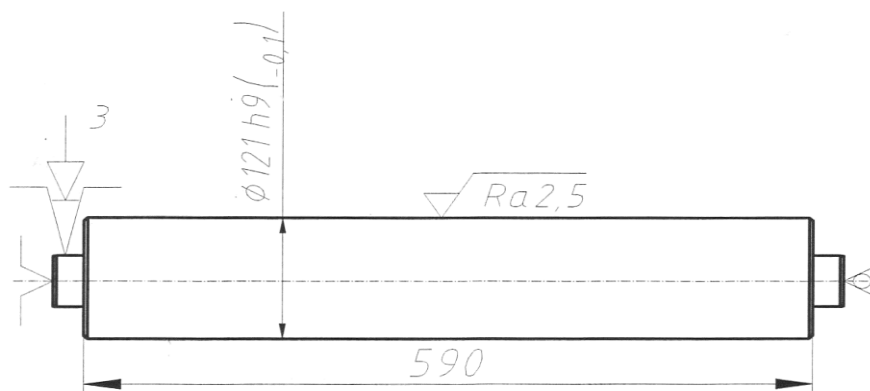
Ескіз обробки деталі "Рейка зубчата ПЭА 01.40.01.603А"
